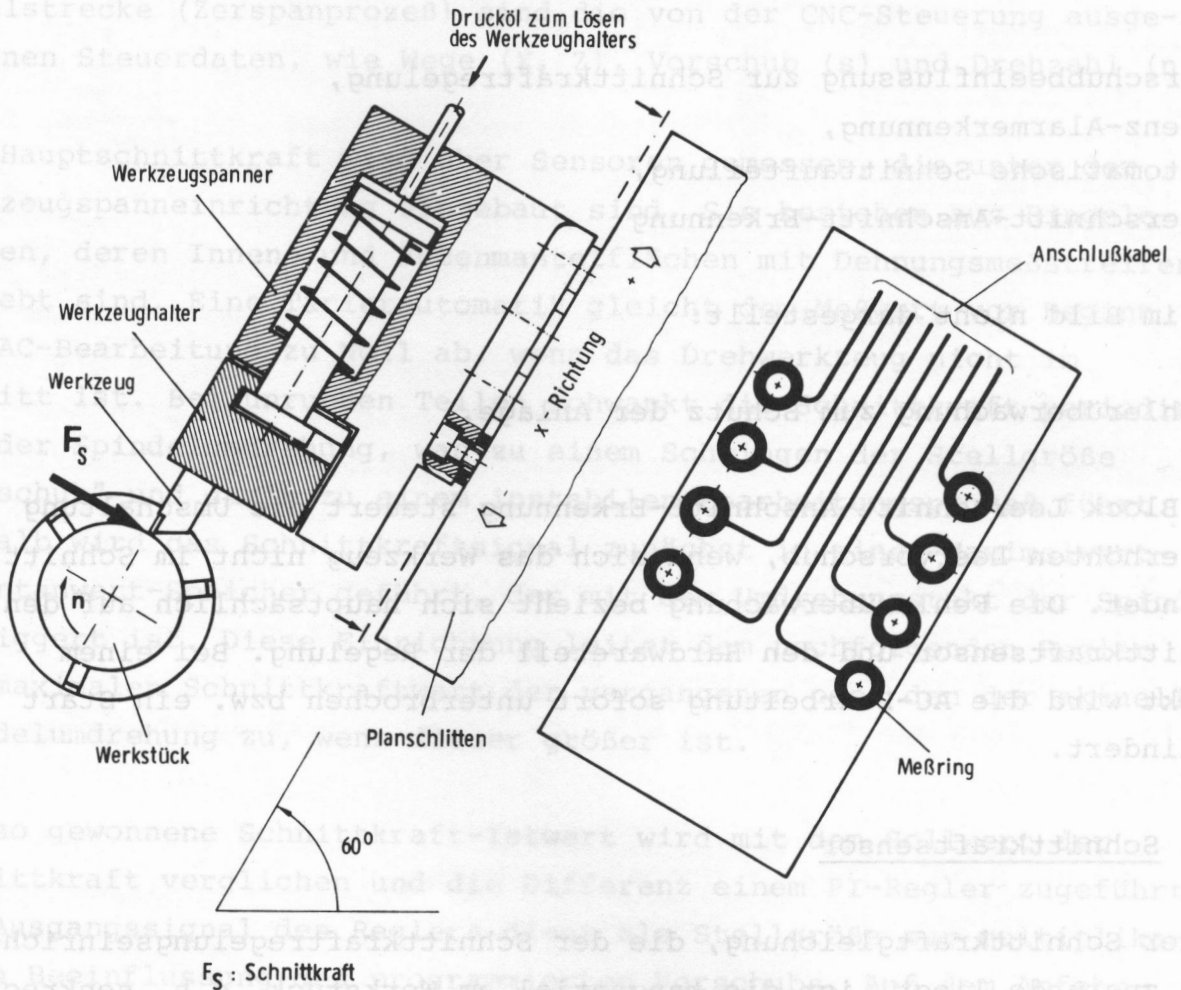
Anordnung des Schnittkraftsensors unter dem Werkzeugwechsler der Drehmaschine
